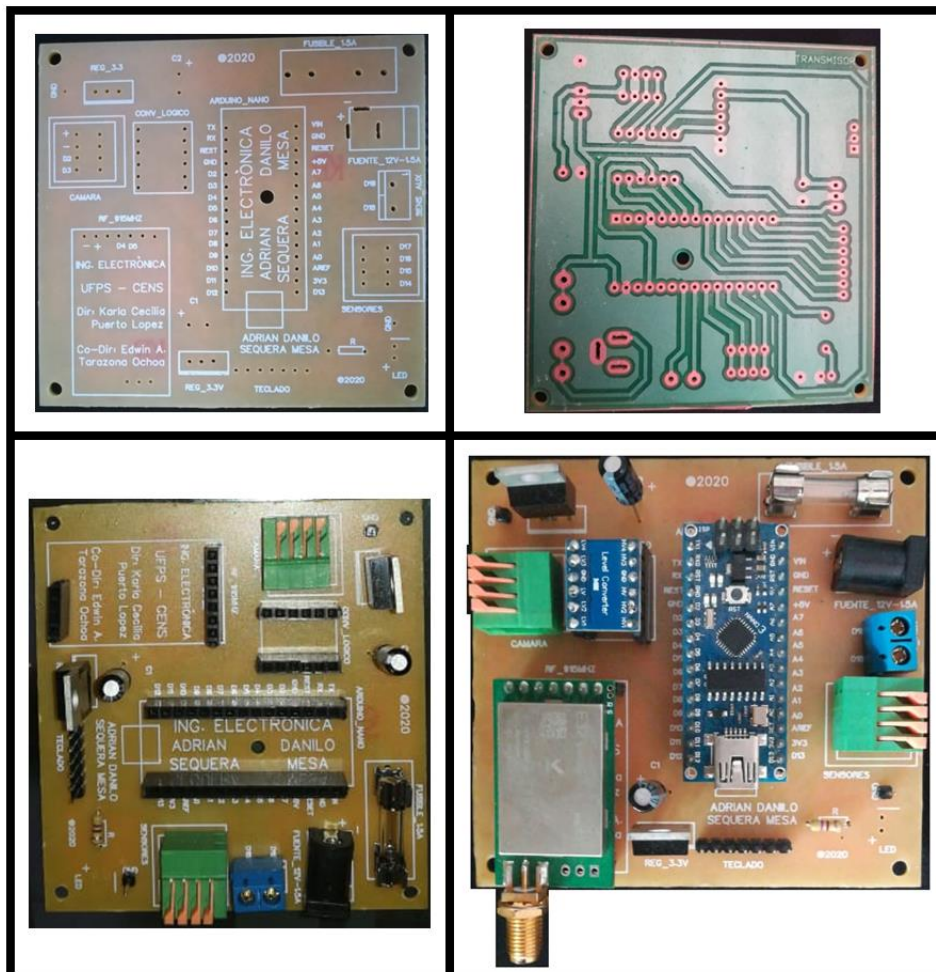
PCB impresa y soldada del circuito transmisor.
